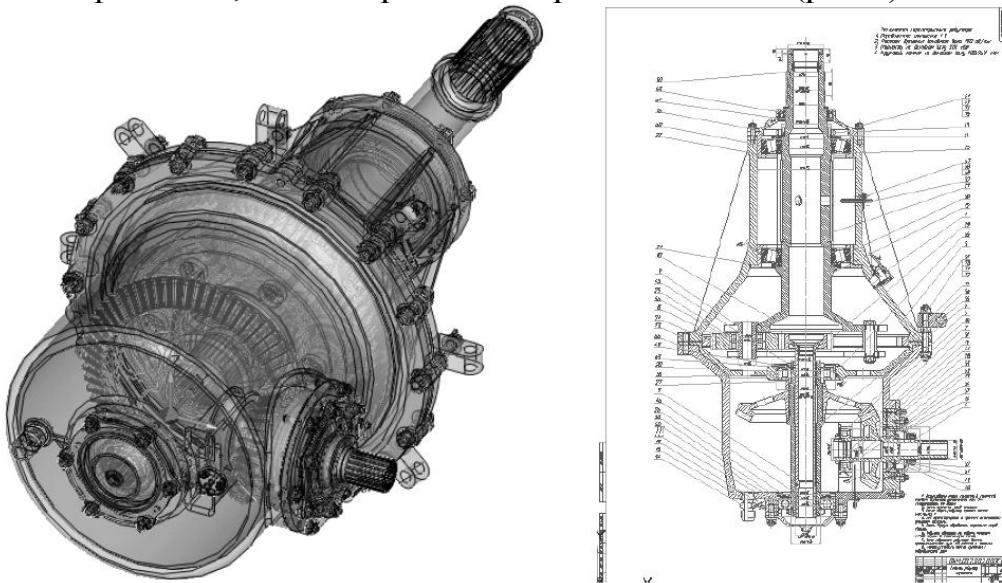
3D-модель редуктора в сборе и созданный на её основе сборочный чертёж
